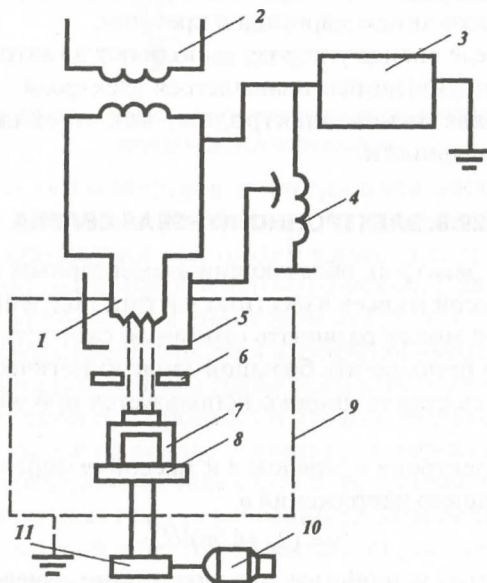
Схема установки для сварки электронным лучом
